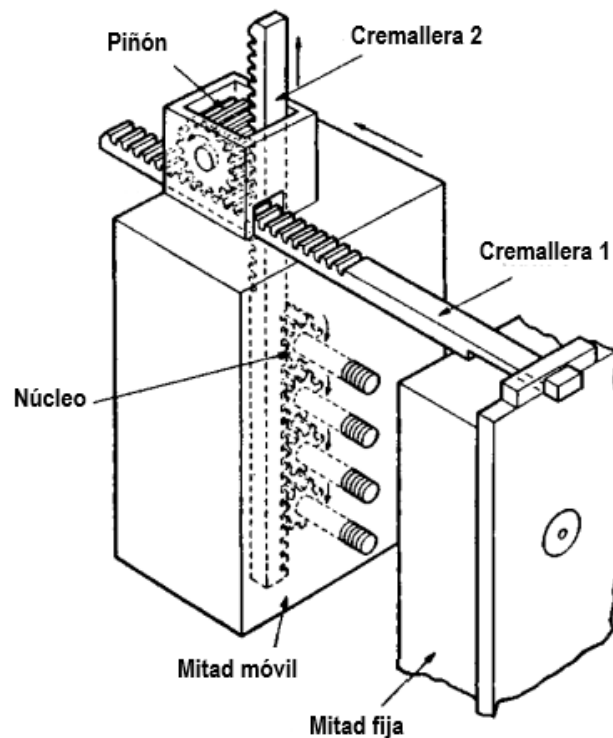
Molde con accionamiento por cremallera. Fuente: How to make injection molds [7].
